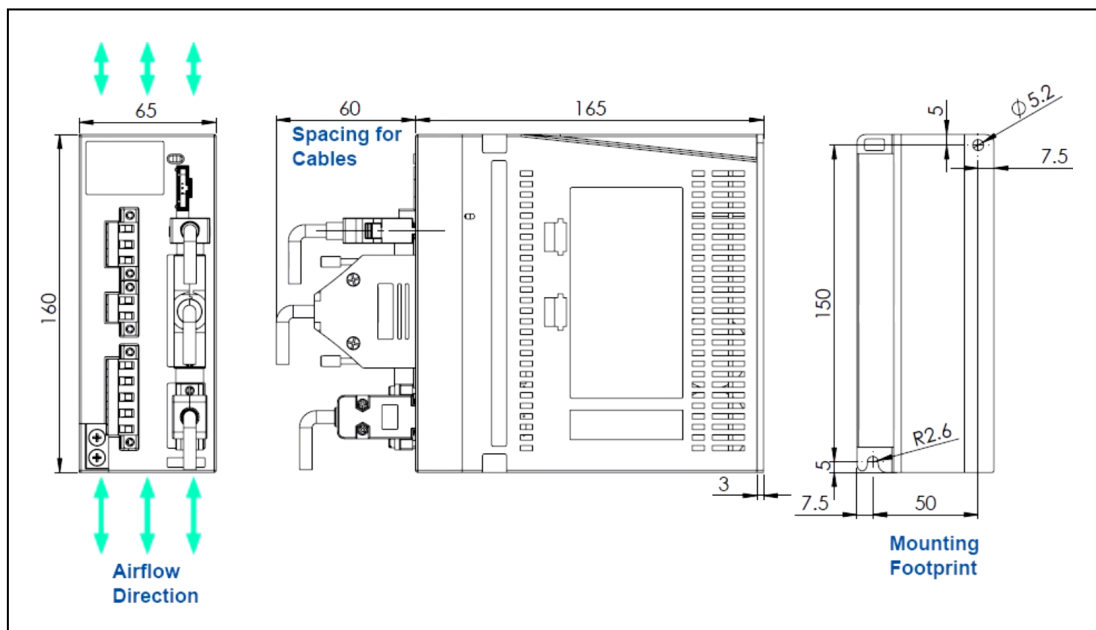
Dimensões em mm do driver que deve acompanhar o motor do *spindle*, incluindo o espaçamento necessário para os cabos e uma indicação do fluxo de ar que deve ser permitido. (DMM Technology, 2021b)
